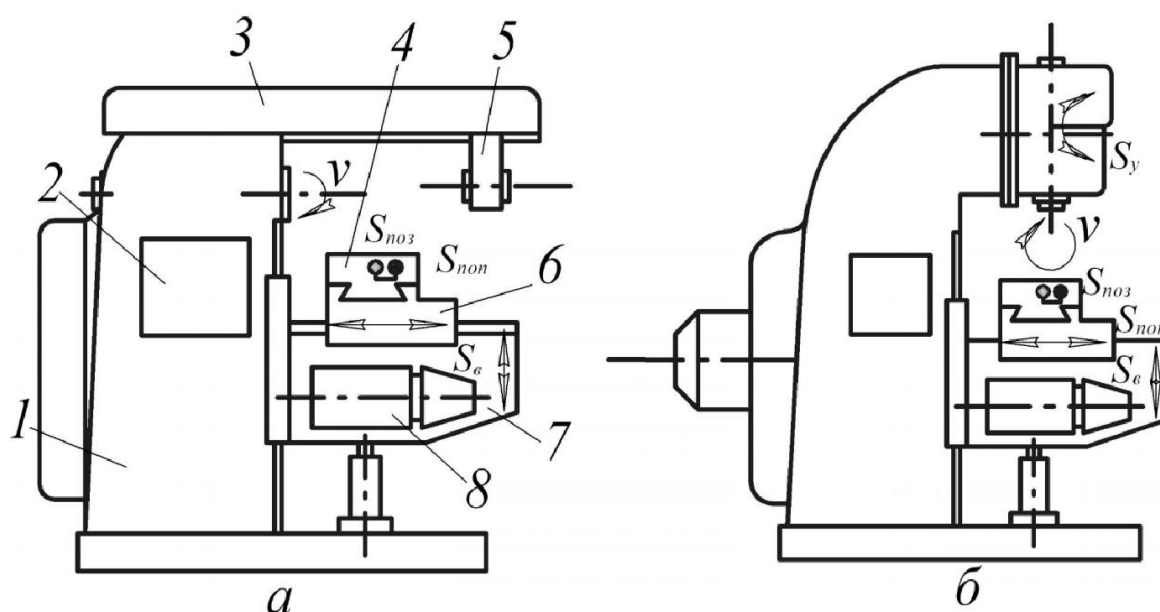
Консольні горизонтально-фрезерний (а)
